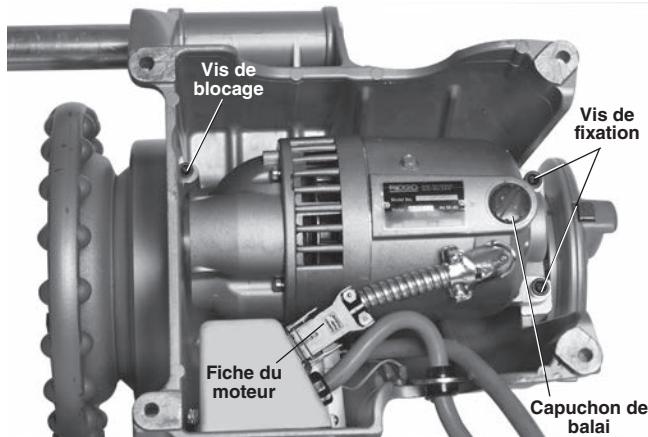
Dépose du carter inférieur du moteur pour le remplacement des balais
